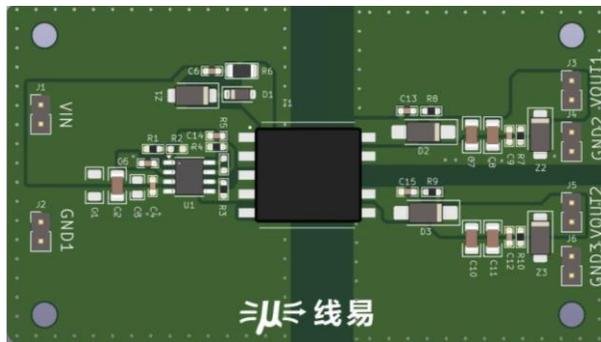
PCB 示意图 (尺寸: 80 x 45mm)
